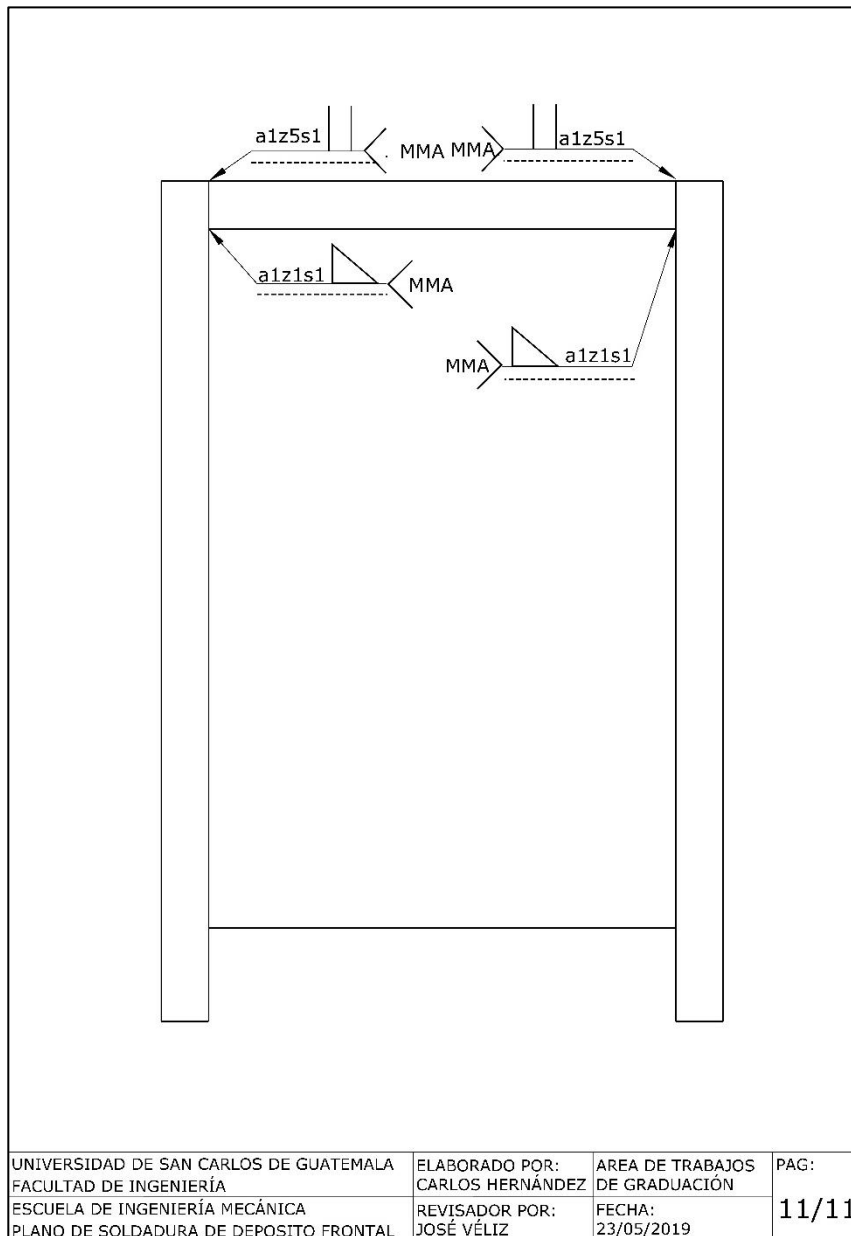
Plano de soldadura del depósito vista planta
